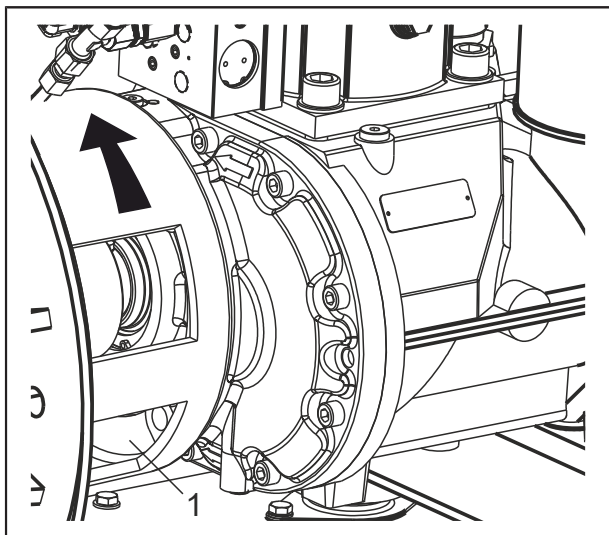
Kontrol af den gearløse kompressors drejeretning
